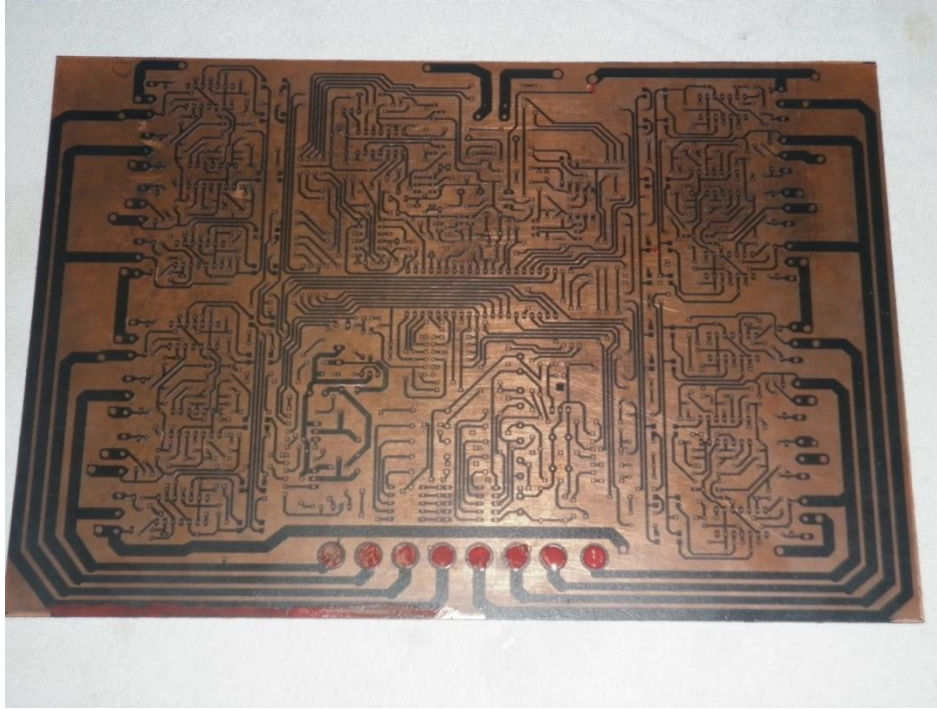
Tarjeta de circuito impreso del inversor multinivel construido.
